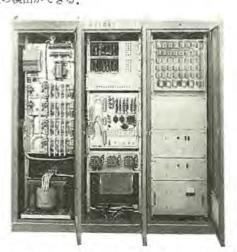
MELDAS-2832 工作機械 ナライ 制御装置 Automatic copying controller for machine tools.
